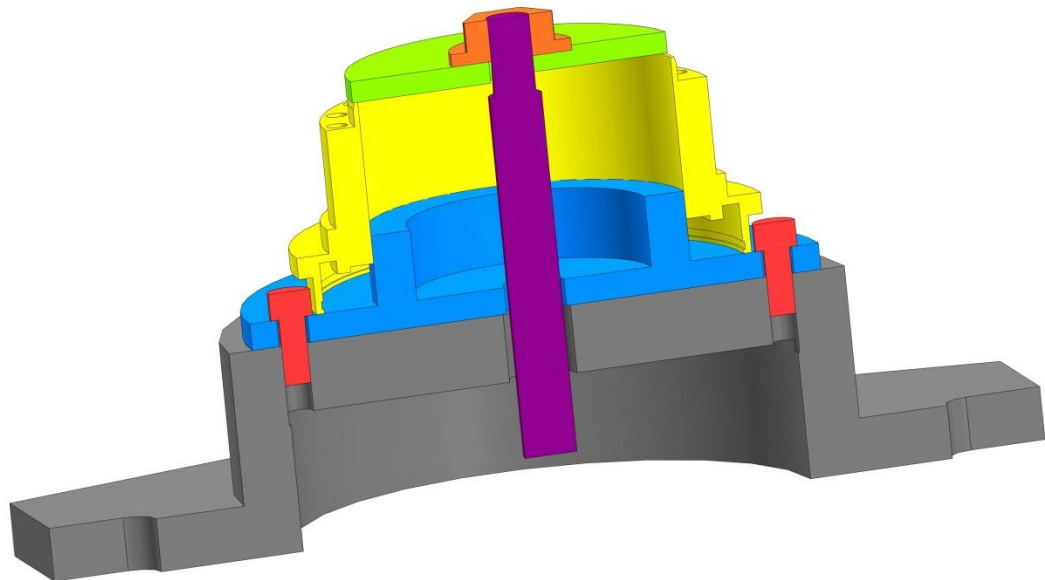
Спроектований верстатний пристрій із деталлю у розрізі
